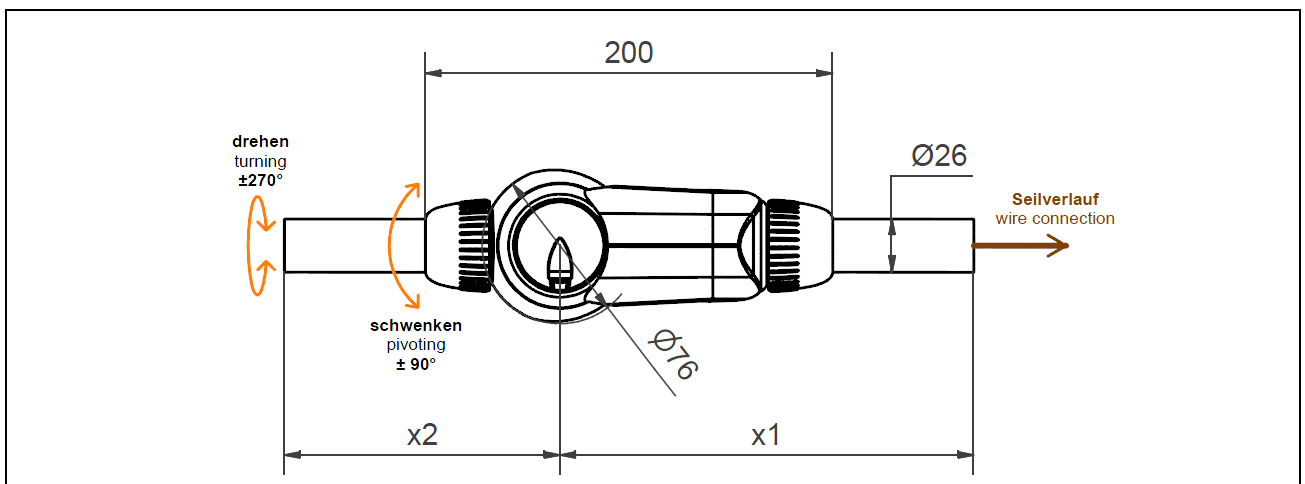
Maßzeichnung 2-Achs-Gelenk RL-50-001
